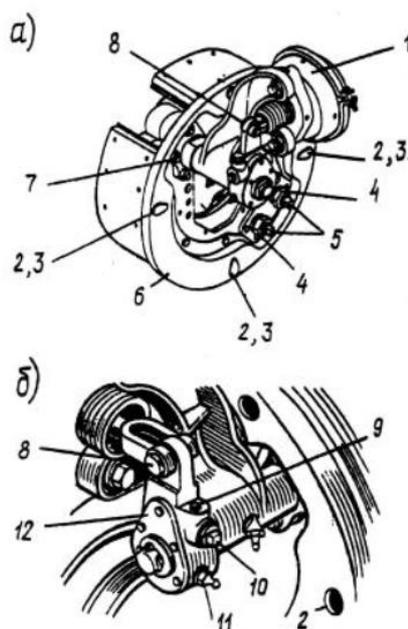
Тормозной механизм переднего колеса (а) и регулировочный рычаг тормозного механизма (б):
